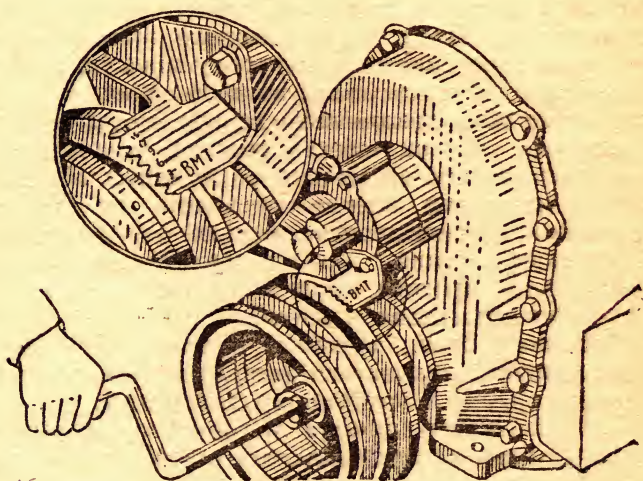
Установка поршня первого цилиндра двигателя ЗИЛ-130 в верхнюю мертвую точку
